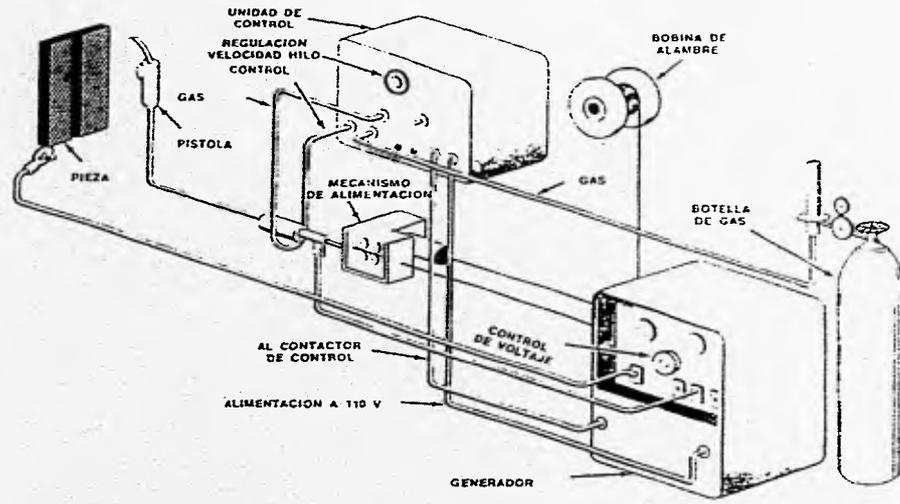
a. INSTALACION Y EQUIPO PARA SOLDADURA MIG.
